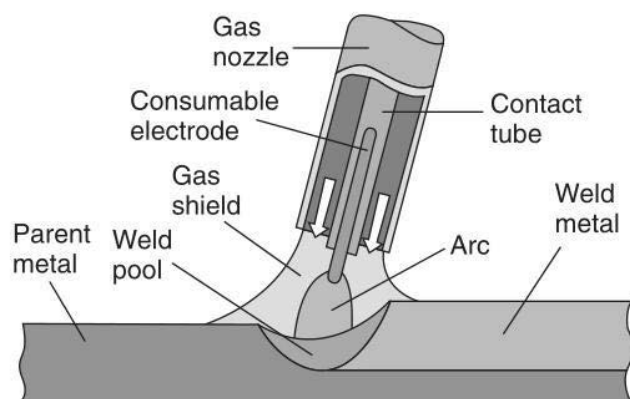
Representação esquemática da soldadura MIG (Kubasek & Vojtech, 2011).
